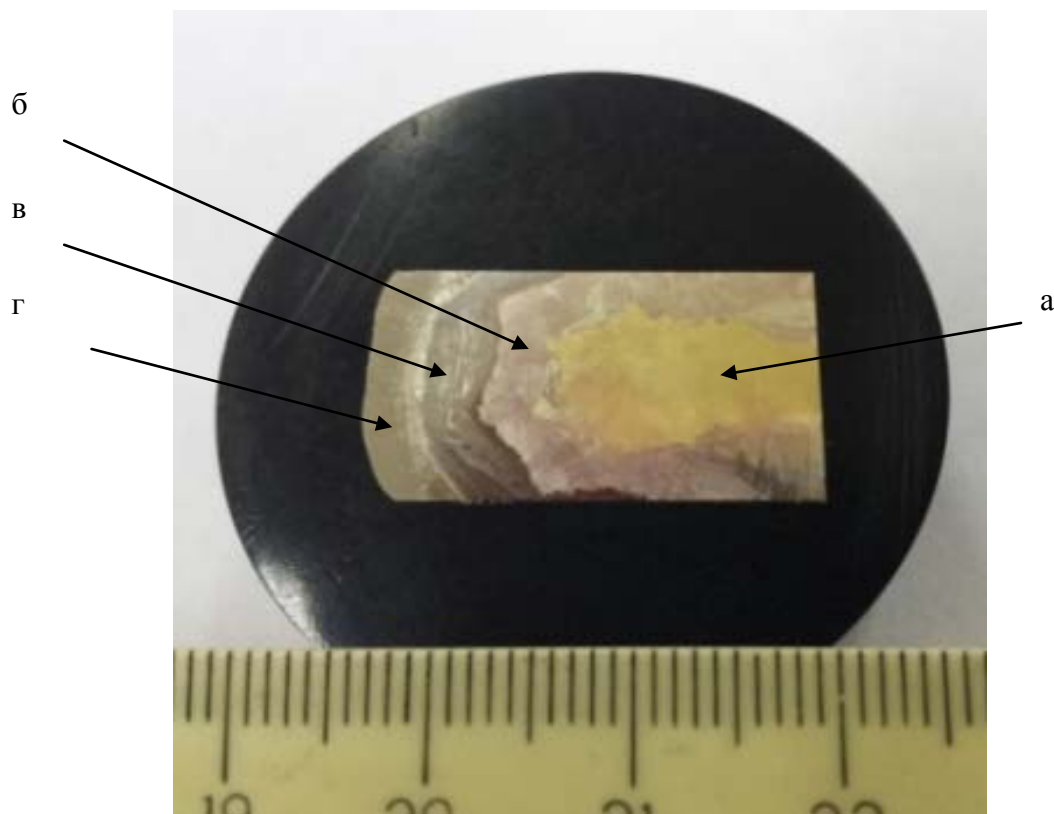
Шлиф соединения, полученного наплавкой маломагнитного подслоя ручным аргодуговым способом неплавящимся электродом на бронзу. Использованные основной металл (а) и сварочные материалы (б-г):
